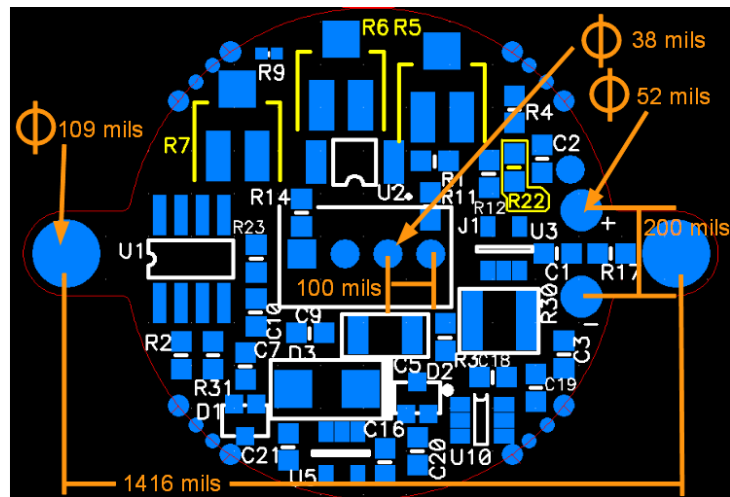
Vue du côté potentiomètre du PCB OEM Standard
